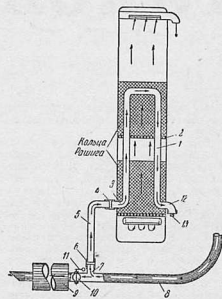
Схема приспособления для подогрева вертикального тонкого очистителя отработанными выхлопными газами двигателя
